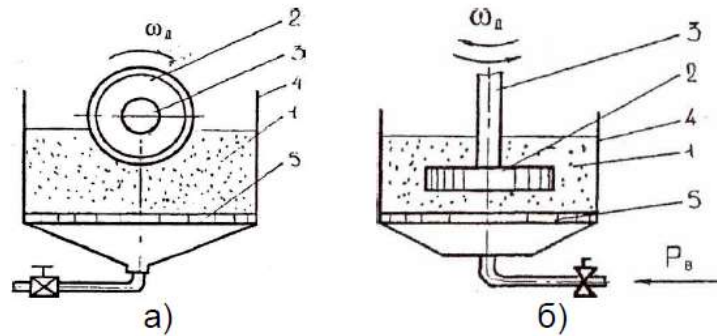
Схеми турбоабразивної обробки : а - одностороннє обертання деталі; б - реверсивне обертання деталі
